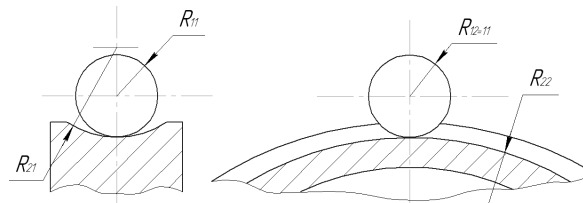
Схема контакта шарика и дорожки внутреннего кольца радиального подшипника
